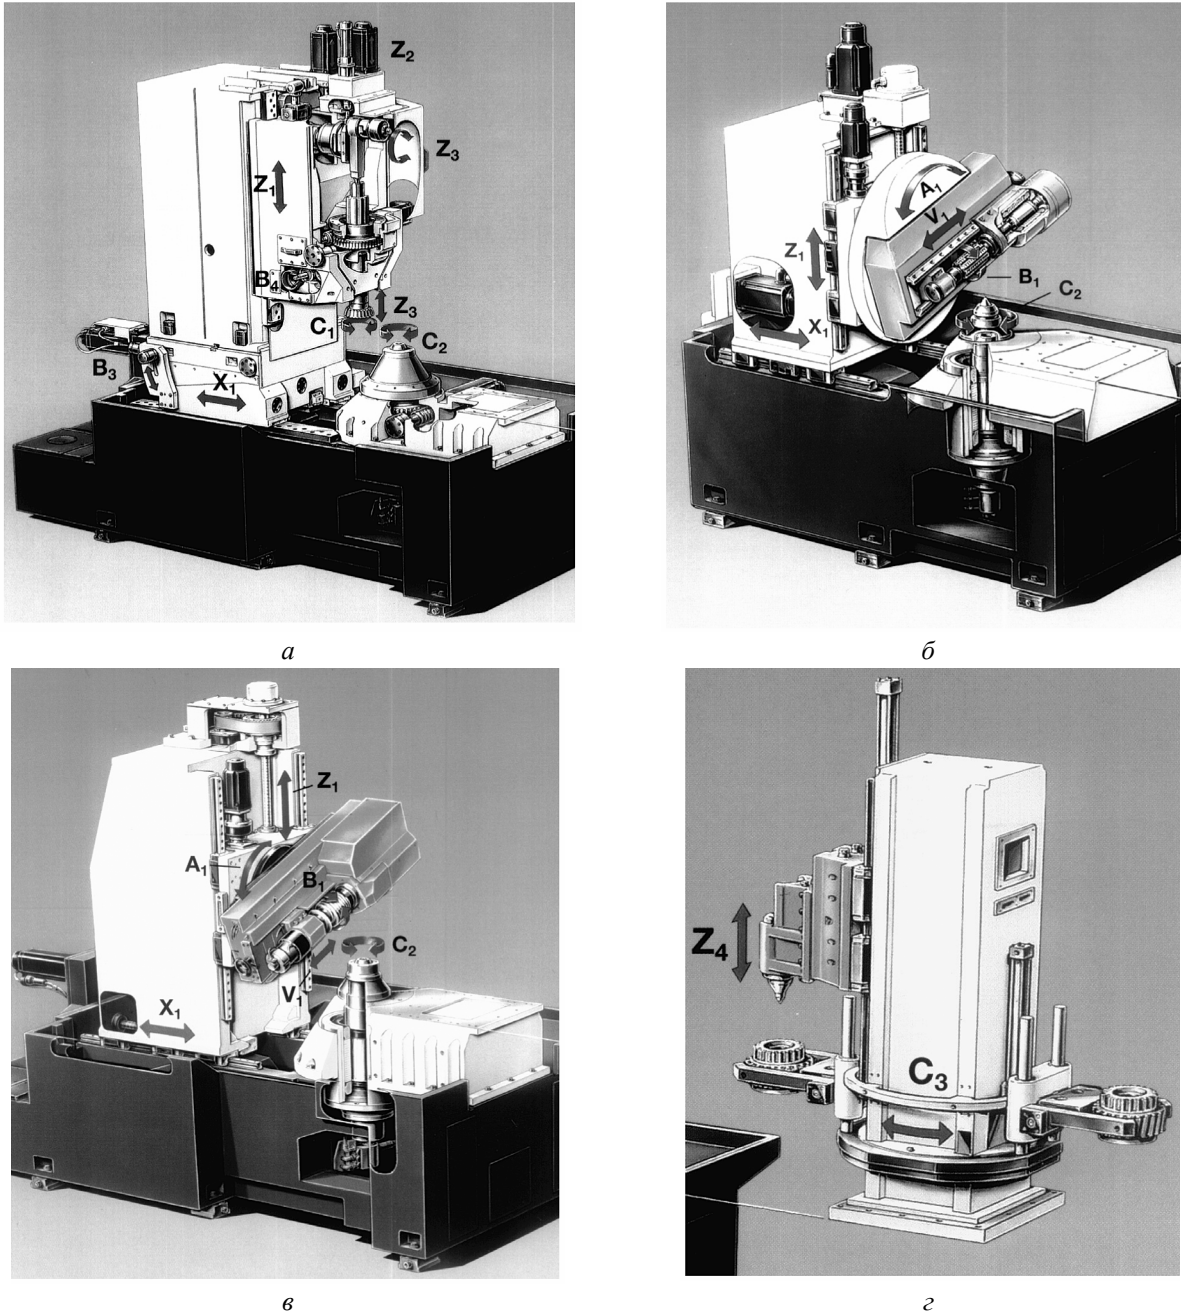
Зубообробні верстати з ЧПК фірми Liebherr-Verzahntechnik GmbH: а – зубодобальний верстат мод. LFS18; б – зубофрезерний верстат мод. LC80 ; в – зубошліфувальний верстат мод. LCS180; г – стійка з механізмом заміни деталей
